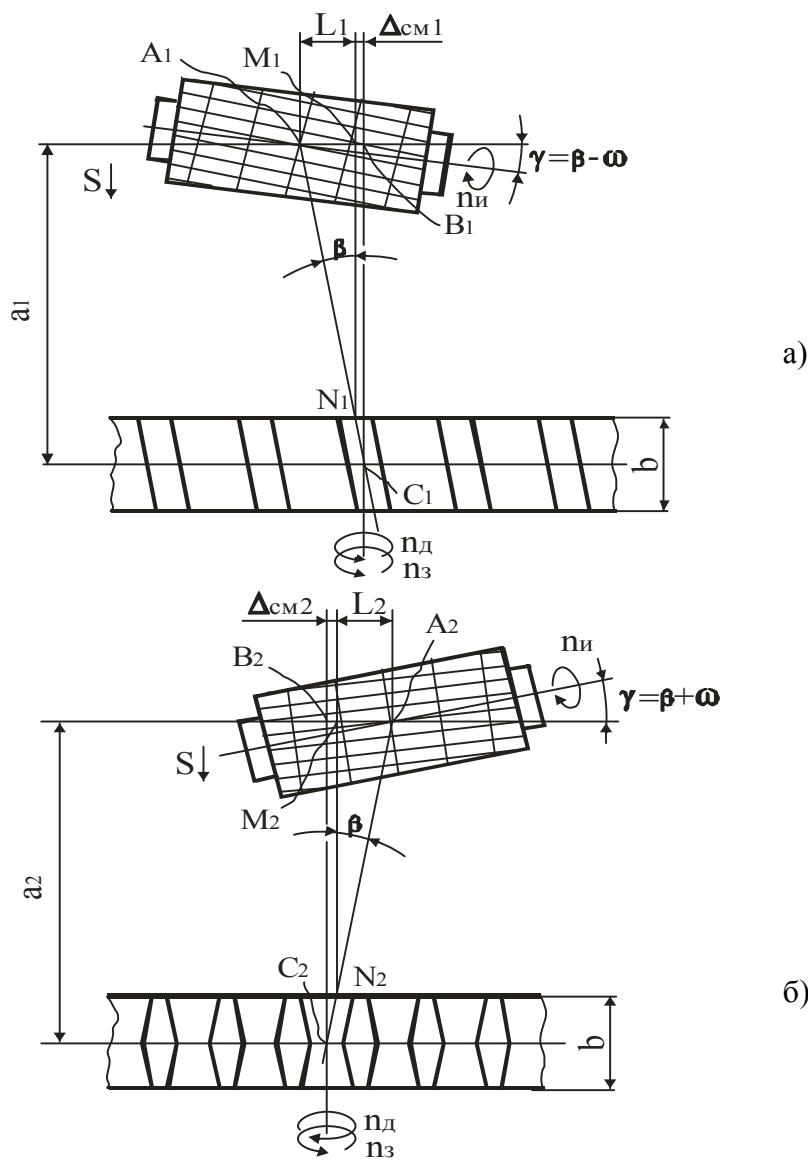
Траектории перемещения инструмента в относительном движении при остановленной заготовке: а) первый рабочий ход; б) второй рабочий ход
